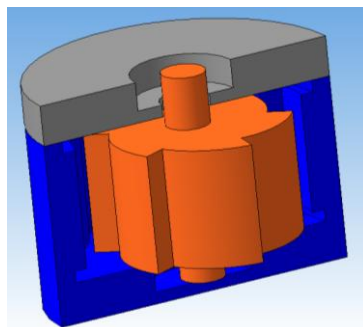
3D модель конструкции ЭГЛД в разрезе.
